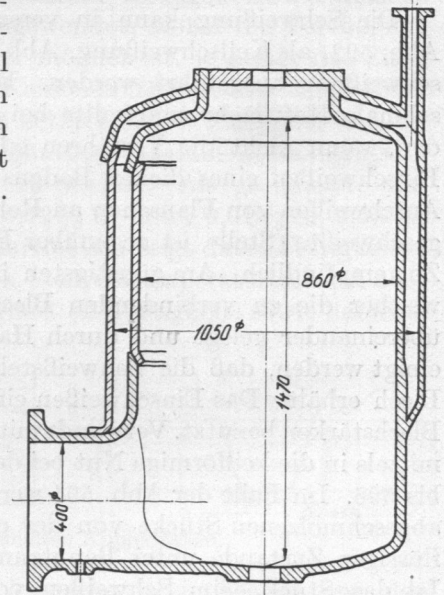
Gefäß mit Heizmantel, geschweißt (J. Pintsch, Fürstenwalde). M. 1 : 25.
